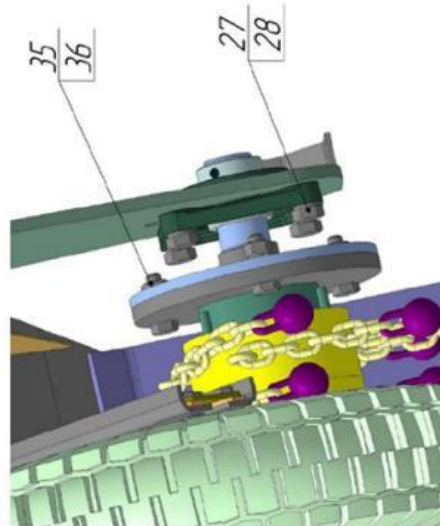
установка фланца приводного вала в подшипниковом узле
